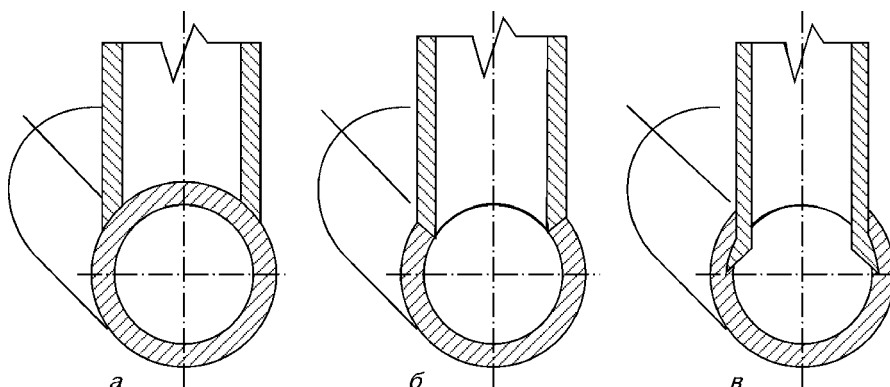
Конструкции тройниковых соединений, изготавливаемых с использованием технологии сваркопайки: а — с формированием внешнего фланца; б — с конусообразной формой шва; в — с формированием внутреннего фланца
